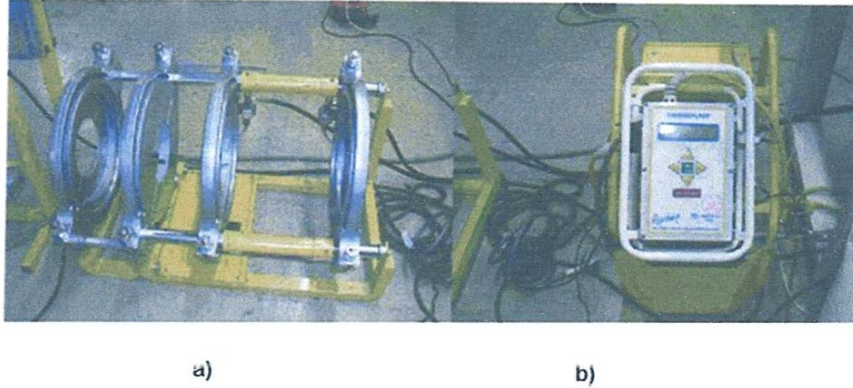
Banc de soudage (a) et boîtier de contrôle (b)
